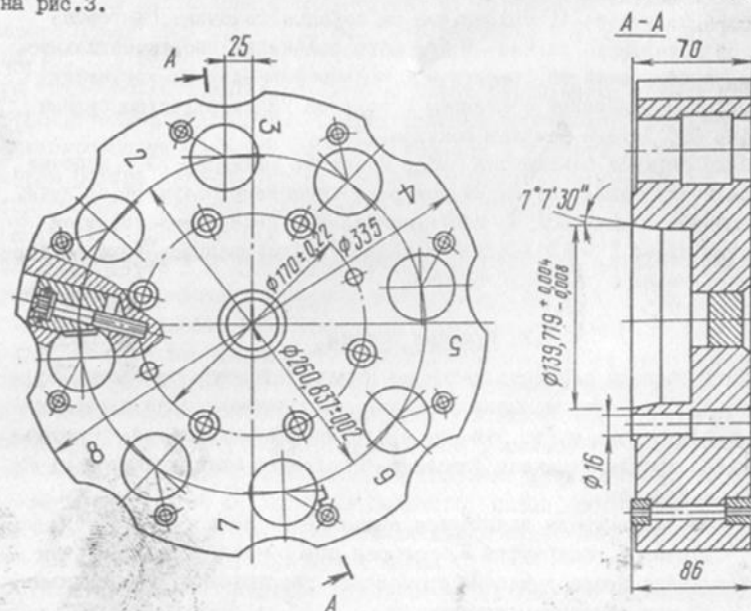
Инструментальный диск восьмипозиционный УГ9326.0300.000
